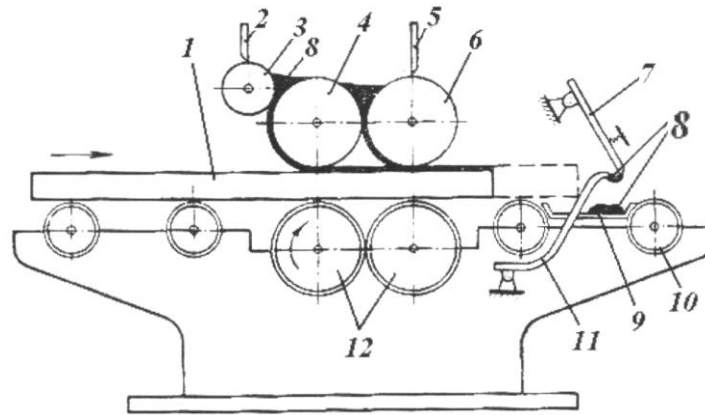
Принципова схема верстата ШПЩ для шпаклювання: 1 - деталь;
